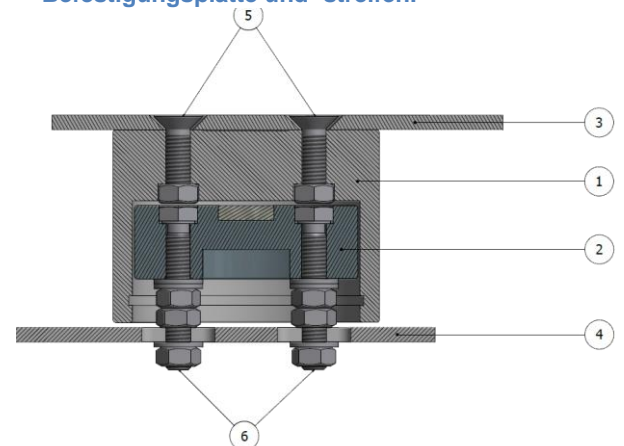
Schematische Zeichnung befestigter Radsensor.
